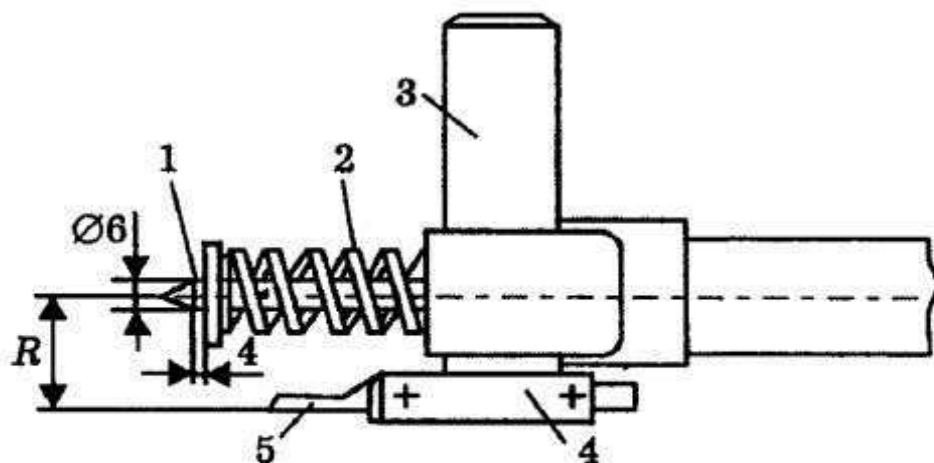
Циркулярный резец: 1 - хвостовик; 2 - пружина; 3 - траверса; 4 - резцедержатель; 5 - резец
